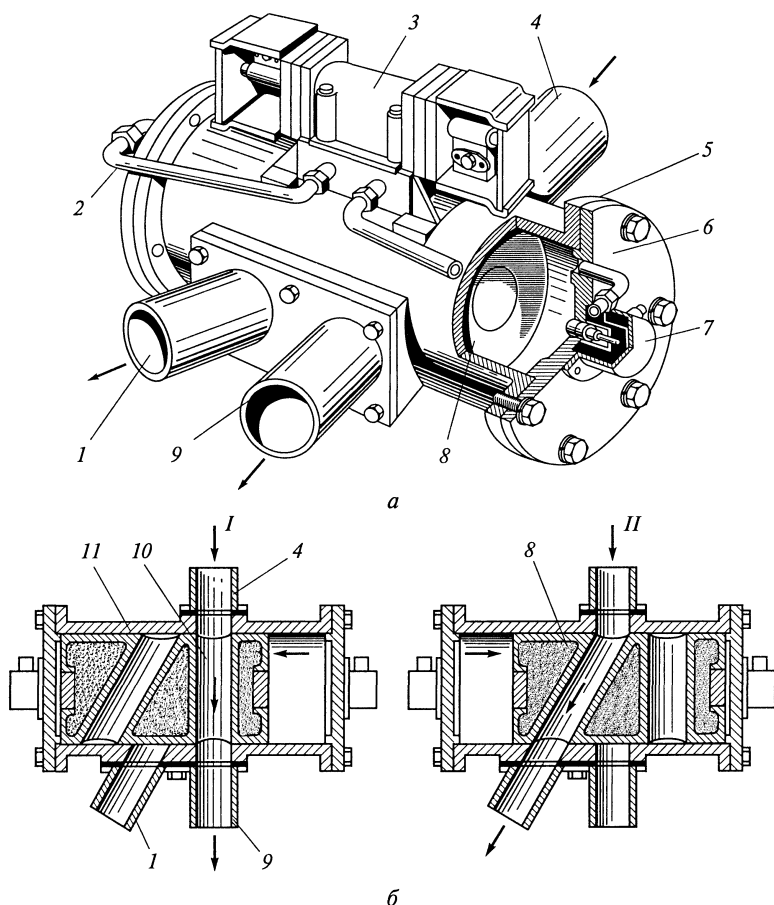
Двухпозиционный переключатель с пневмоприводом:
